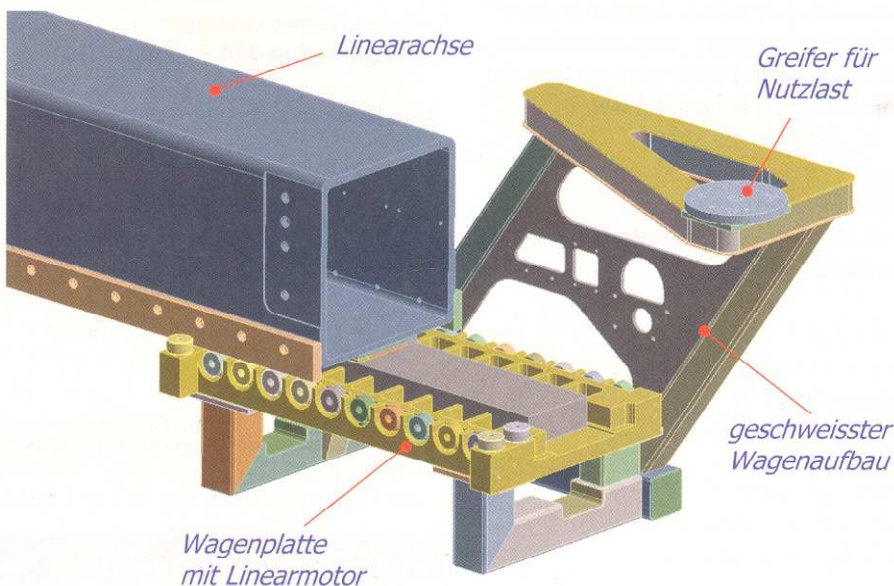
Geschweisster Laufwagen einer Linearachse mit Linearmotor der Firma Güdel AG.
